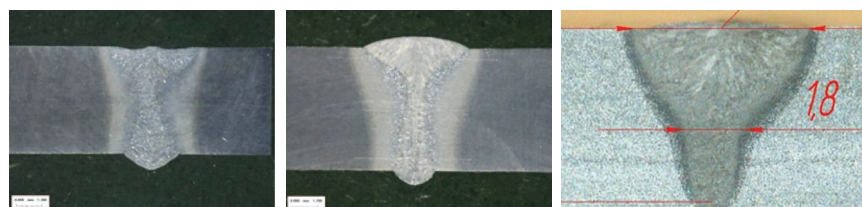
Образец лазерной сварки со средним и широким формированием шва, толщиной 6 мм: а) лазерная сварка в среде защитного газа  $K=1,4$ , б) лазерная сварка с присадочной проволокой, в) пример сварного шва с широким формированием шва  $K=1$
